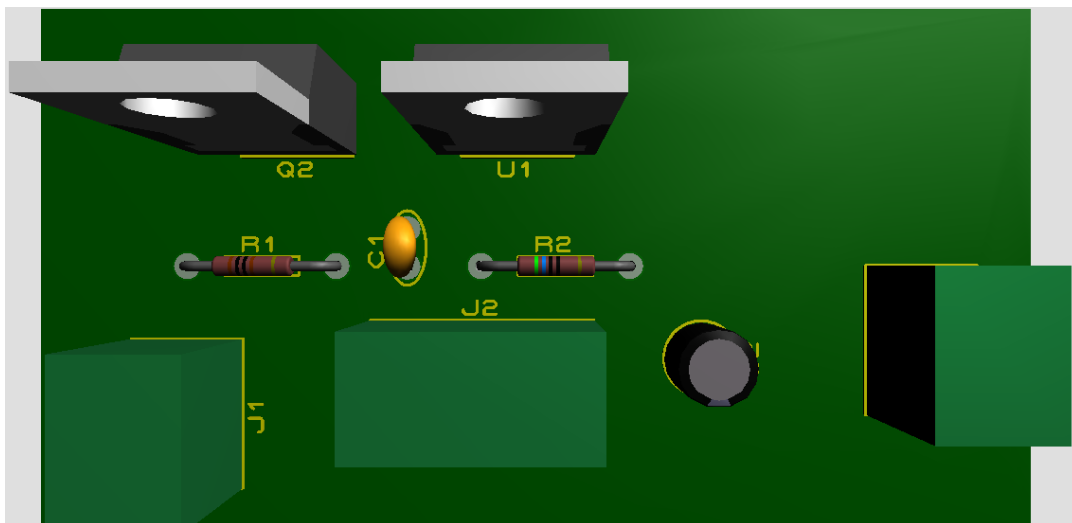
Vista de la placa PCB en 3D del Regulador de Voltaje.
